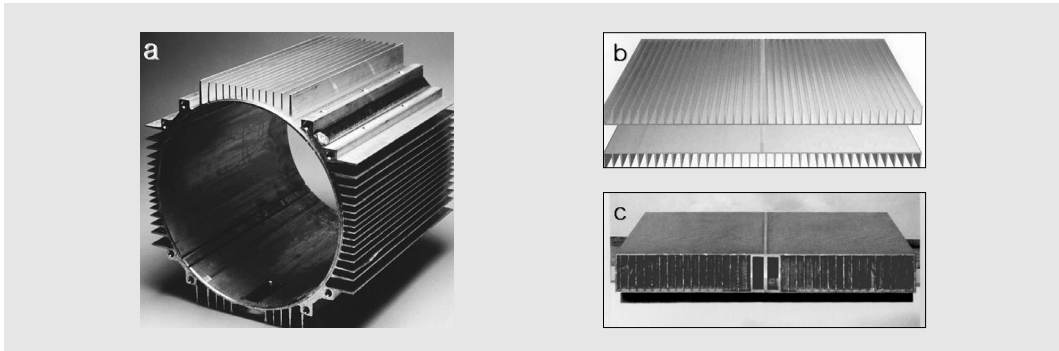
(a) Motor housing, (b) 알루미늄 heat sink panel
